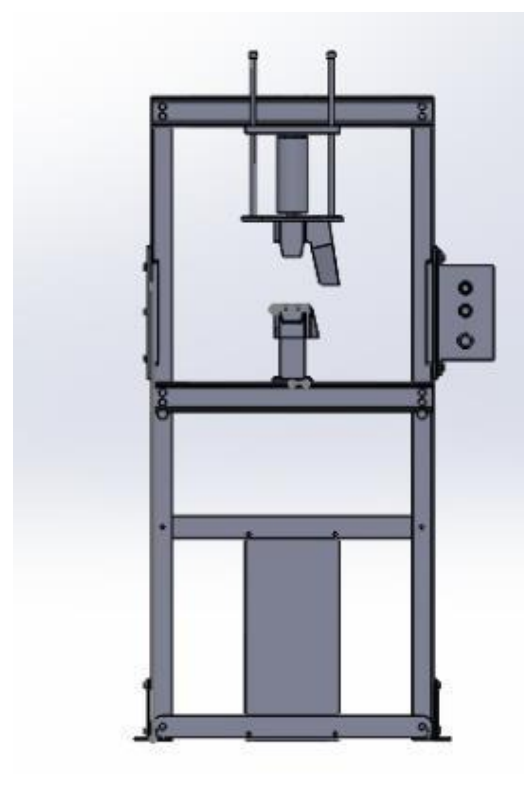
diseño de máquina completa, con todos los accesorios. (vista derecha)
